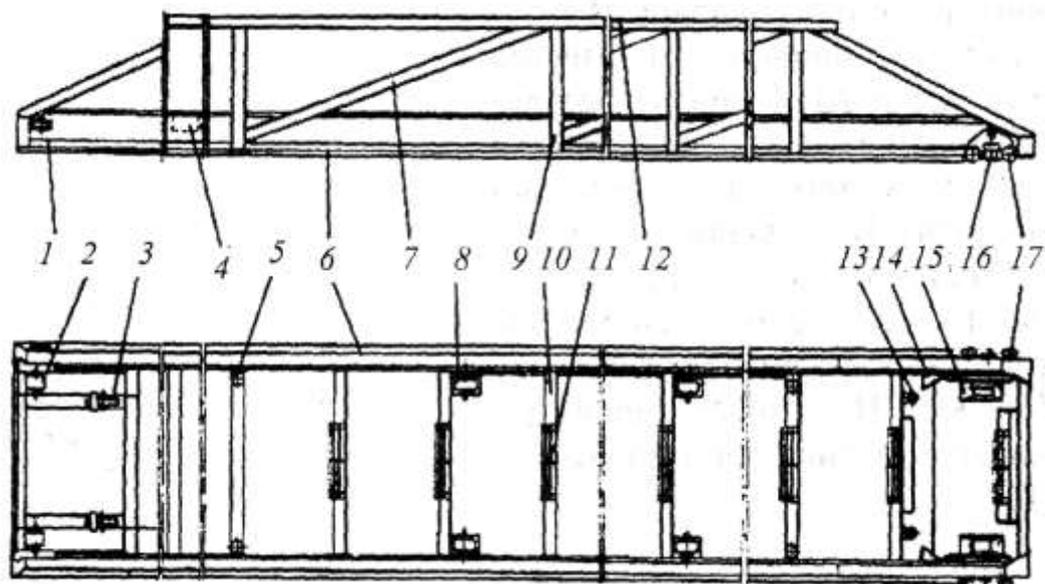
Колено лестницы: 1 - ролик направляющий; 2 - передний опорный ролик; 3 - блок; 4 - упор; 5 - опорная шайба; 6 - нижний пояс (тетива); 7 - раскос; 8 - средний опорный ролик; 9 - стойка; 10 - ступень; 11 - накладка резиновая; 12 - верхний пояс; 13 - ось качалки натяжного устройства; 14 - упор; 15 - замыкатель; 16 - ось балансирующего кронштейна; 17 - задний опорный ролик
